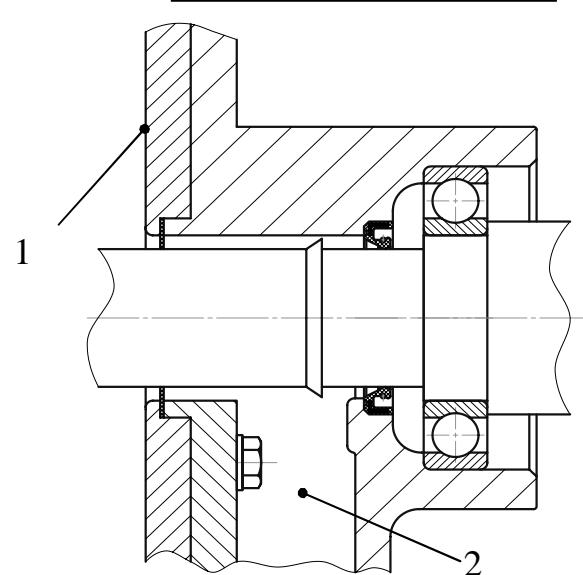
Вузли опор валів: 1 - поверхня контакту із продуктом; 2 - повітряний проміжок.
